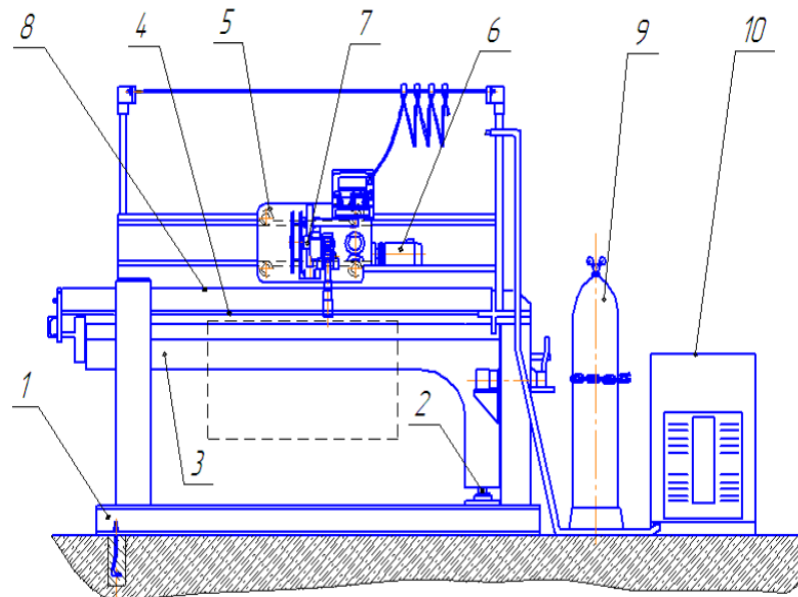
Стенд для збирання поздовжніх стиків обичайок: 1 – підставка; 2 – вісь; 3 – поворотна консоль; 4 – рама з клавішними пневмопритискачами; 5 – механізм поздовжнього переміщення зварювальної головки; 6 – електропривод; 7 – зварювальна головка Мультитрак А2 (GMAW); 8 – жолоб з вогнетривкого матеріалу; 9 – газовий балон; 10 – джерело живлення ESAB LAF.
